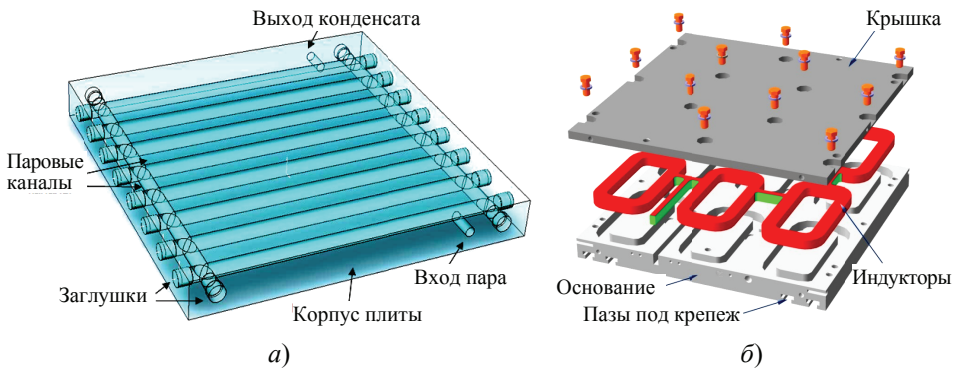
Конструкции нагревательных плит прессов парового (а) и индукционного (б) нагрева
